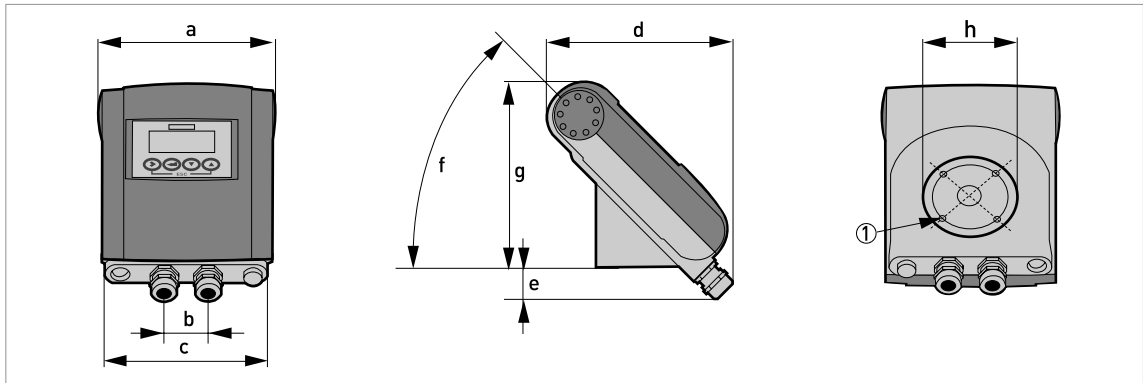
Размеры корпуса компактного исполнения из алюминия (версия 45°)
